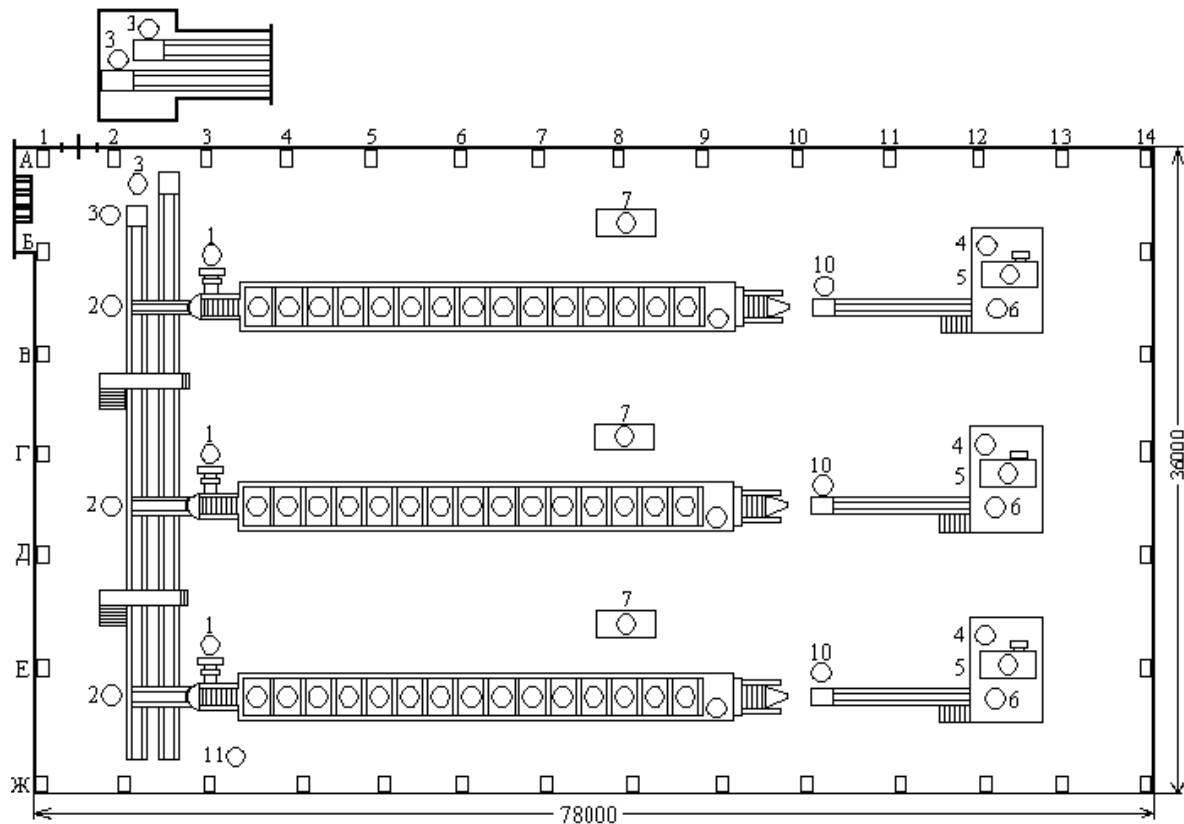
Схематичний план шихтового корпусу цеху.
